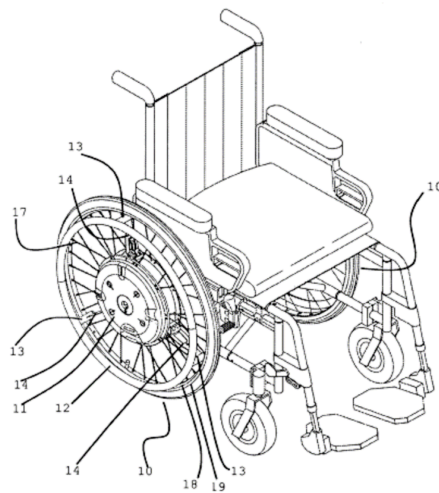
Vista general de la silla de ruedas con el sistema aplicado a la rueda derecha [3]
